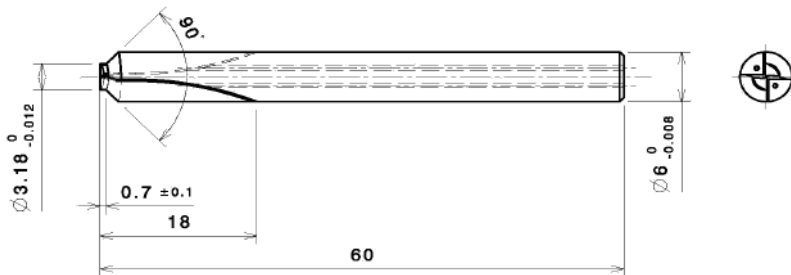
Креслення твердосплавного свердла BOF D3.18X0.7X 60-6 зі сплаву UF10
